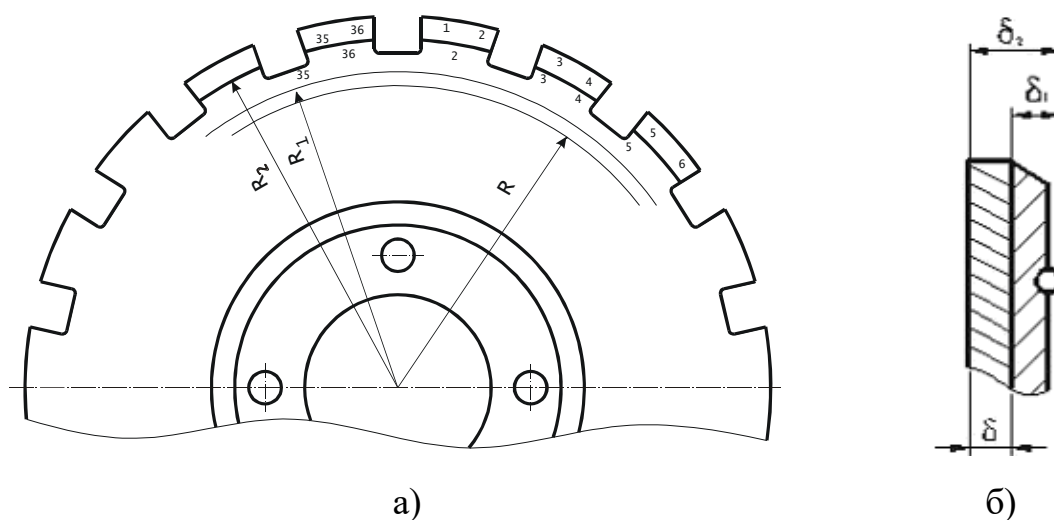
а – елемент, підготовлений для вимірювання товщини наплавленого металу; б – переріз в зоні наплавлення
